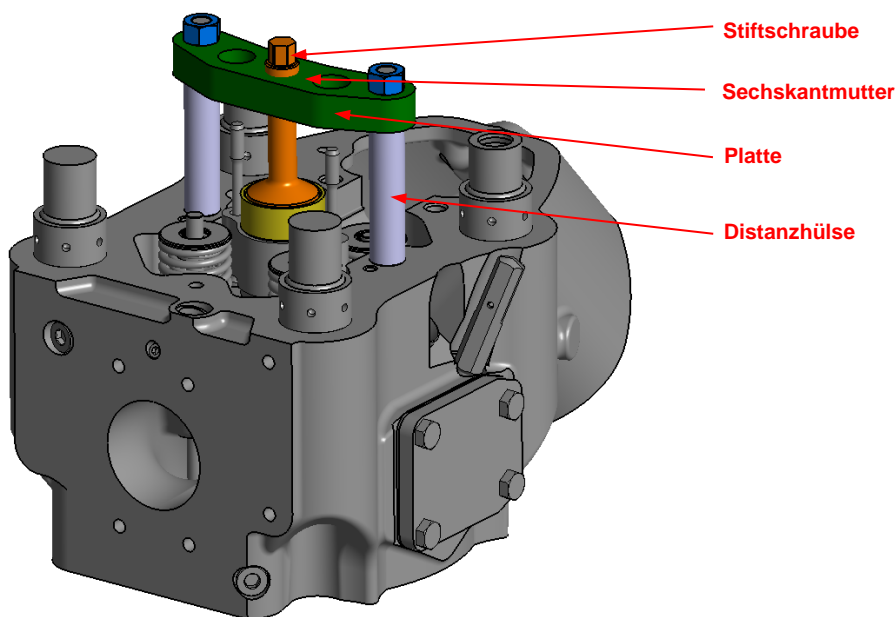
Montage des Vorkammermontagewerkzeugs auf "F"-Zylinderkopf
